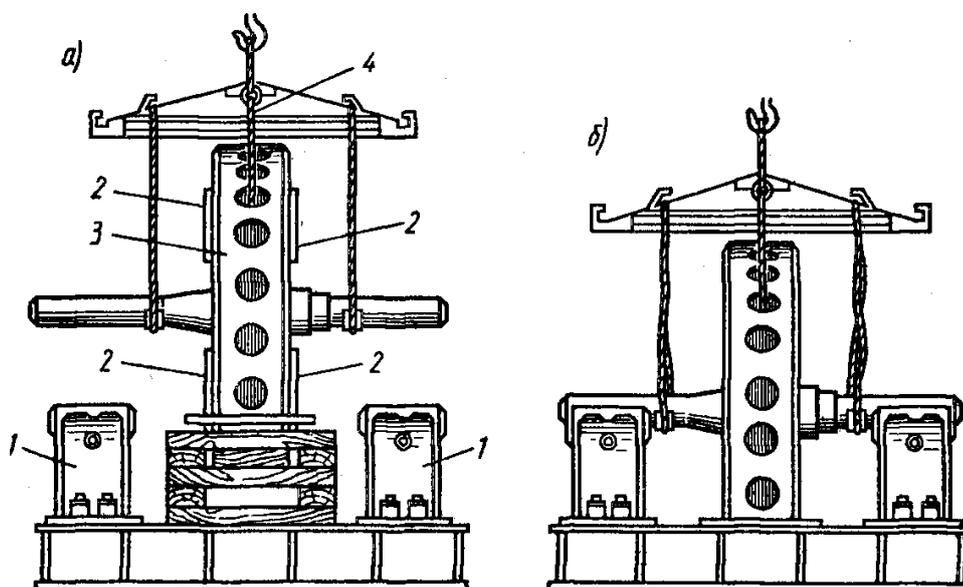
Ввод ротора в статор: *а* — строповка и подъем статора и ротора;
